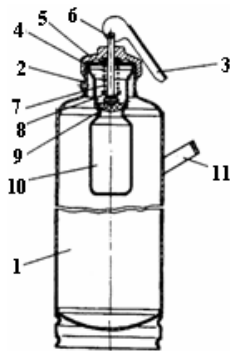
Вогнегасник хімічно-пінний ОХП-10: 1 - корпус; 2 - сопло; 3 - важіль запуску; 4 - кільце ущільнювача; 5 - кришка; 6 - шток; 7 - пружина; 8 - шайба напологлива; 9 - клапан; 10 - стакан; 11 - ручка.
